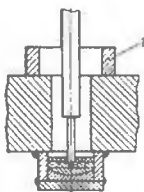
Схема зварювання наскрізного отвору електрошлаковим способом;
